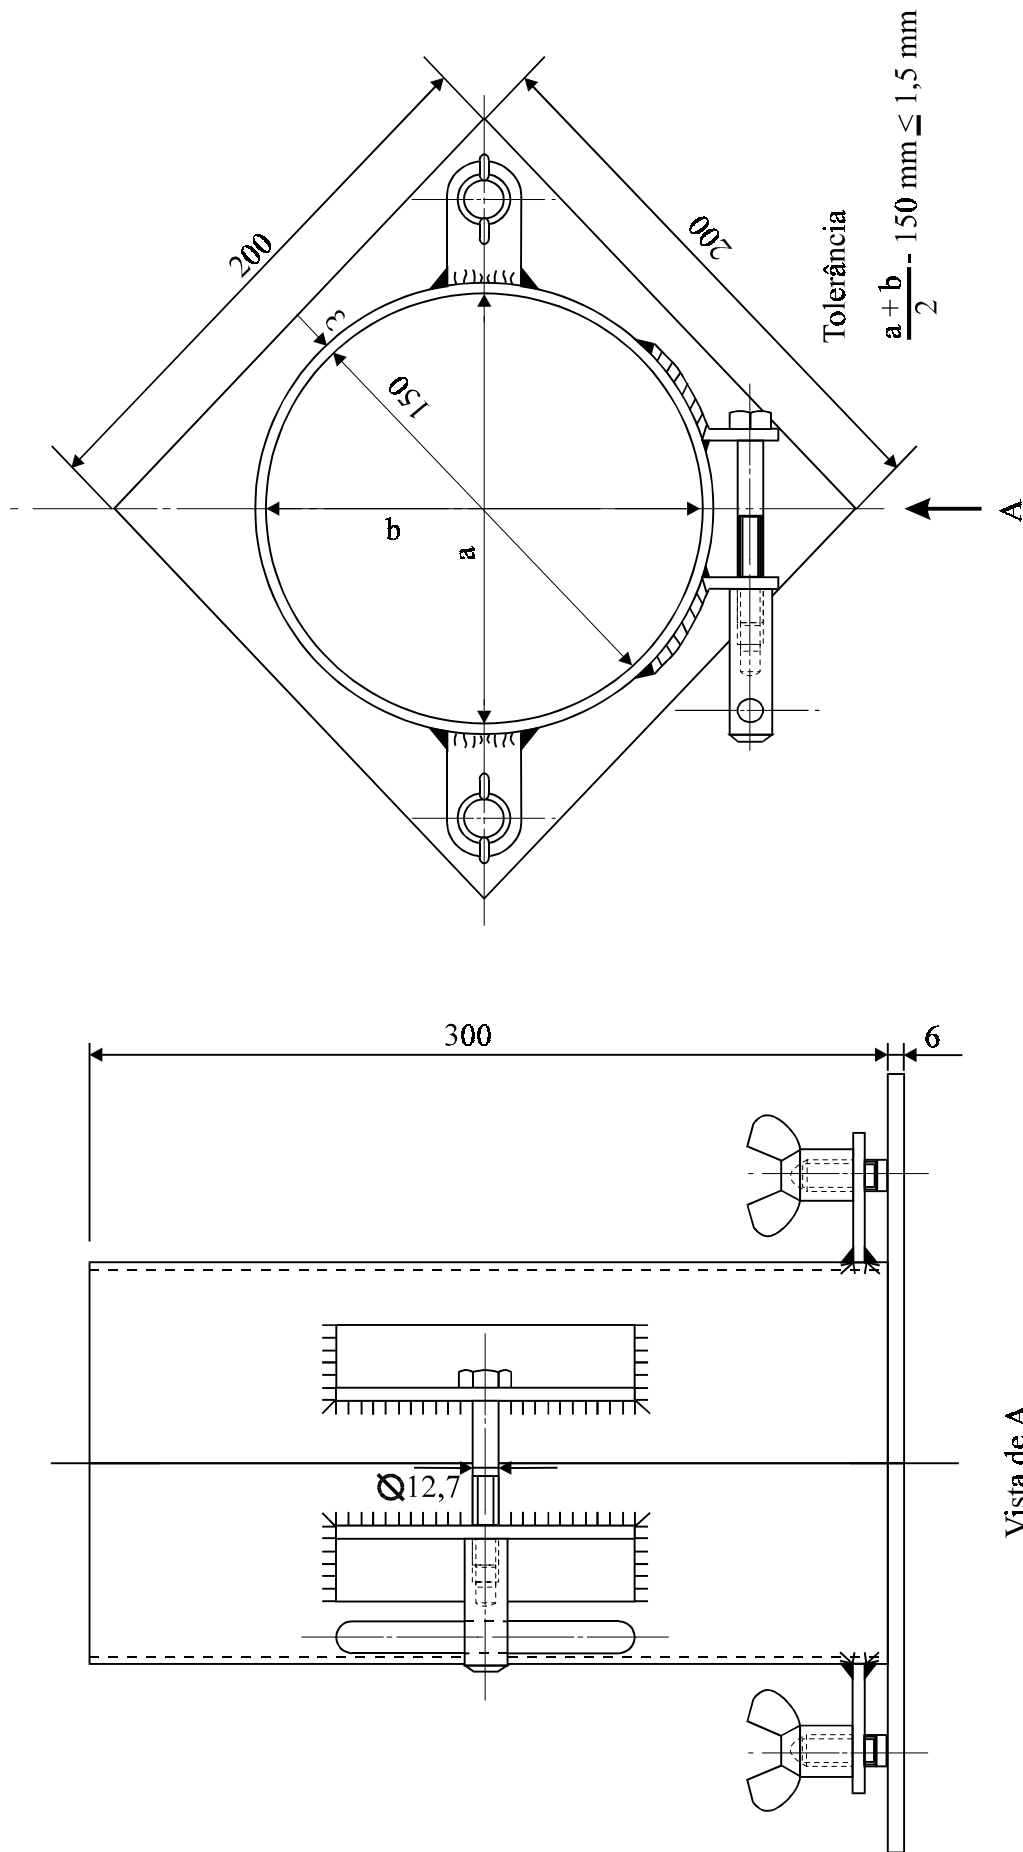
Molde cilíndrico de dimensão básica 150 mm
